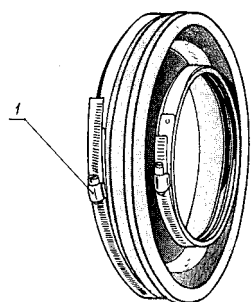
Торцовый уплотнитель (обтюратор)
